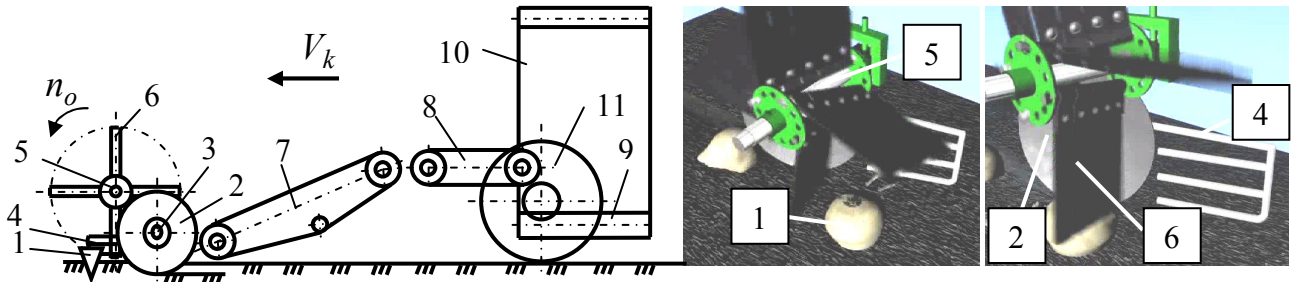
Схема лабораторно-польової установки: 1 – коренеплід; 2 – диск; 3 – вісь; 4 – корененапрямник; 5 – приводний вал; 6 – очисні лопаті; 7, 8, 9, 10 – поздовжній похилий, горизонтальний, поперечний, вивантажувальний транспортери; 11 – колесо
